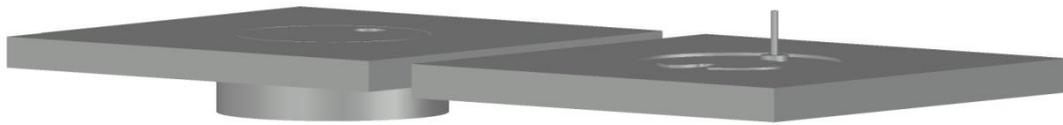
Molde para la pieza 1.2 tapa pequeña. Detalle inferior.
